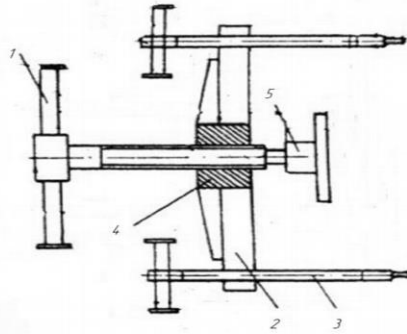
Пристрій для зняття гальмівного барабана з використанням заводських різьбових отворів у барабані мод. УТ-2510: 1 – ручка подачі; 2 – основа; 3 – кріпильний болт; 4 - маточина-гайка; 5 – опора болта подачі;
